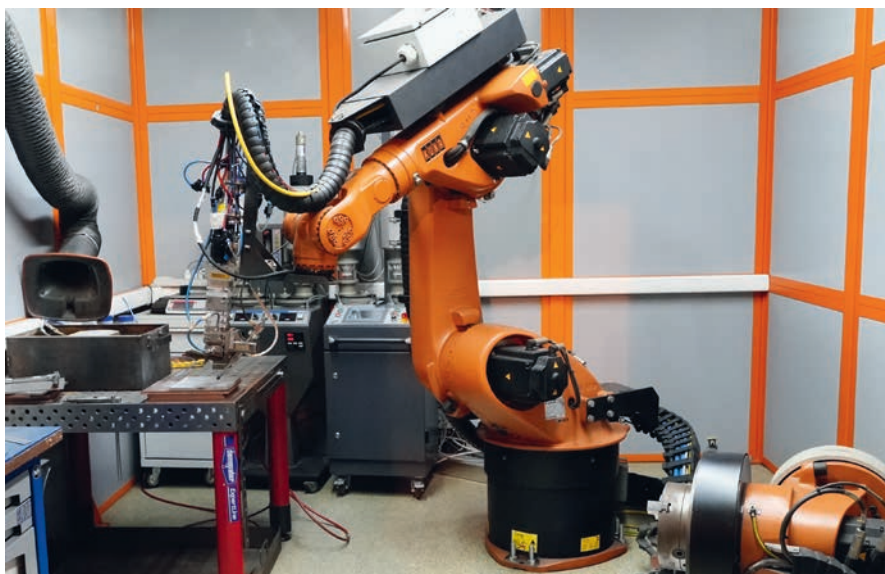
Установка гибридной сварки. Фото: «НТО «ИРЭ-Полюс»
